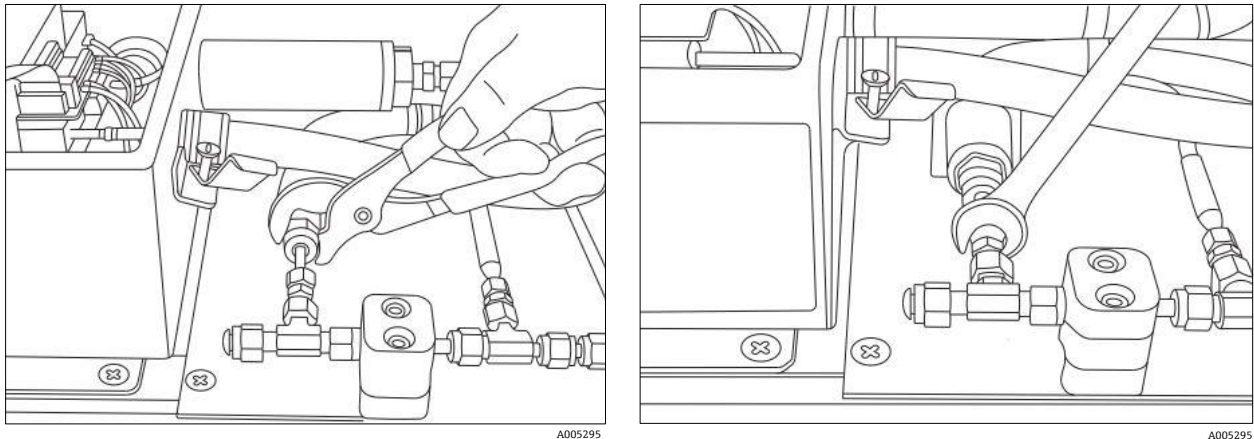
Die Kappe der Kabelverschraubung lösen (links) und die Rohrmutter entfernen (rechts)
